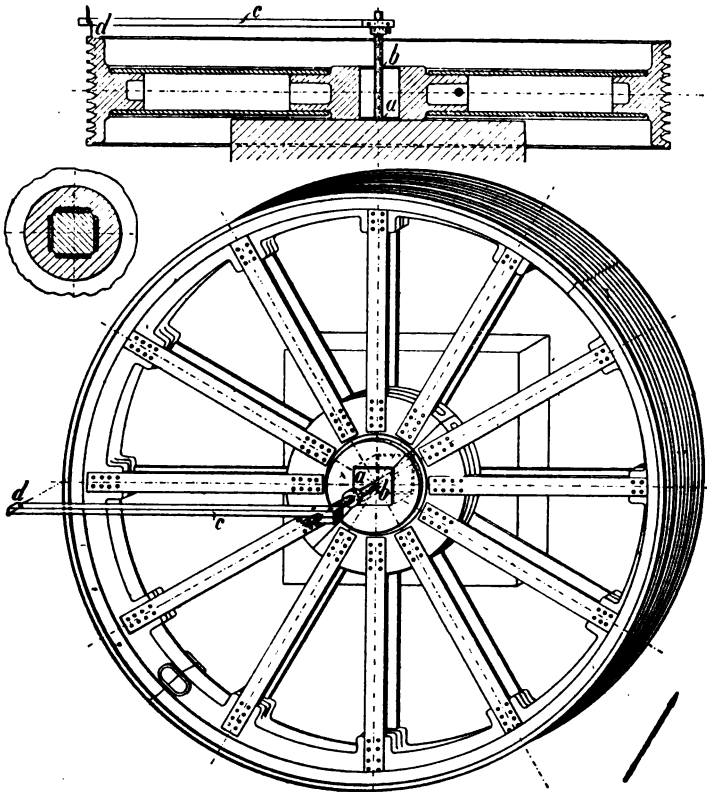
655. Ausrichten von grossen Seilscheiben.
